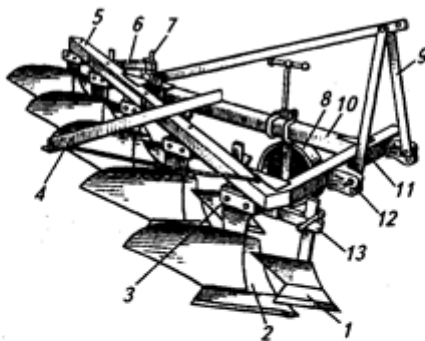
Навесной плуг ПЛН-5-35: 1 – предплужник; 2 – корпус; 3 – угольник для крепления корпусов; 4 – прицепка для борон; 5 – главная балка; 6 – кронштейн крепления ножа; 7 – дисковый нож; 8 – опорное колесо; 9 – навеска; 10 – продольная балка; 11 – поперечная балка; 12 – кронштейн навески; 13 – кронштейн предплужника
